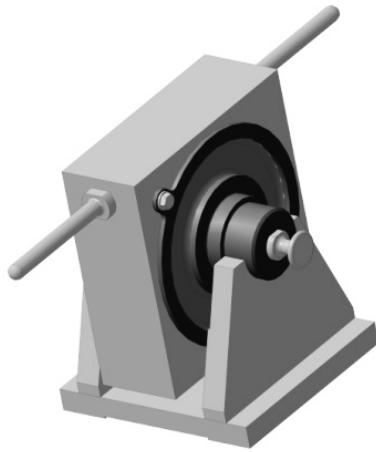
Схема приспособления для испытаний кольца резинометаллического
